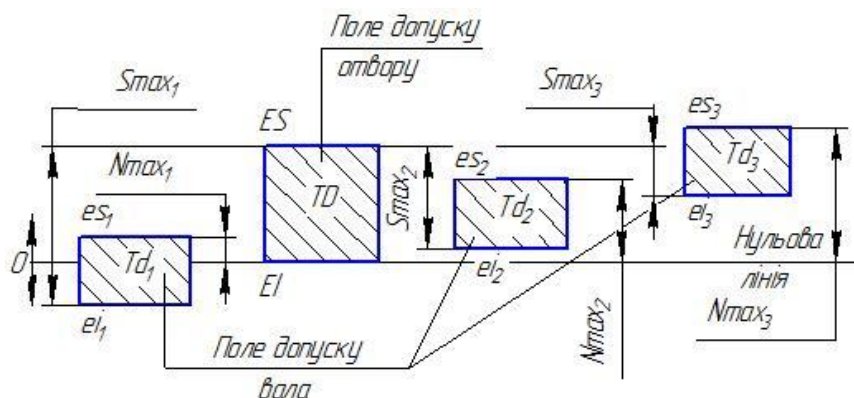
Схема розташування полів допусків перехідної посадки
